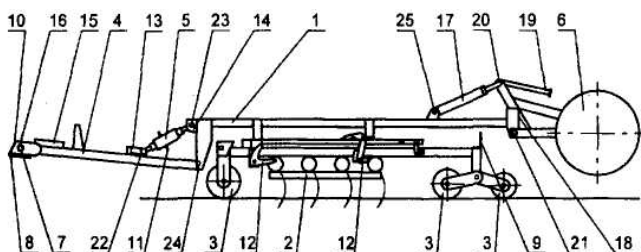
Агрегат комбинированный почвообрабатывающий АКШ-3,6 (вид сбоку):
